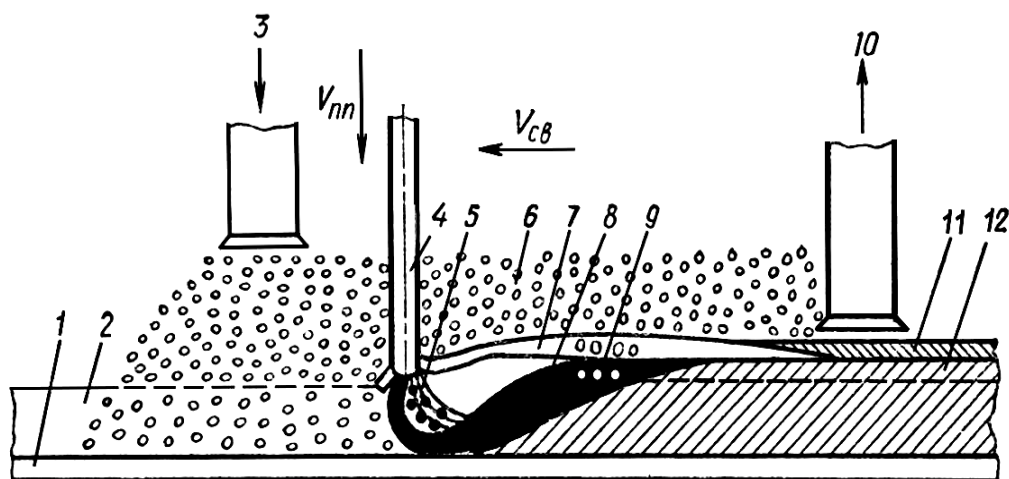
Схема автоматической сварки под флюсом
